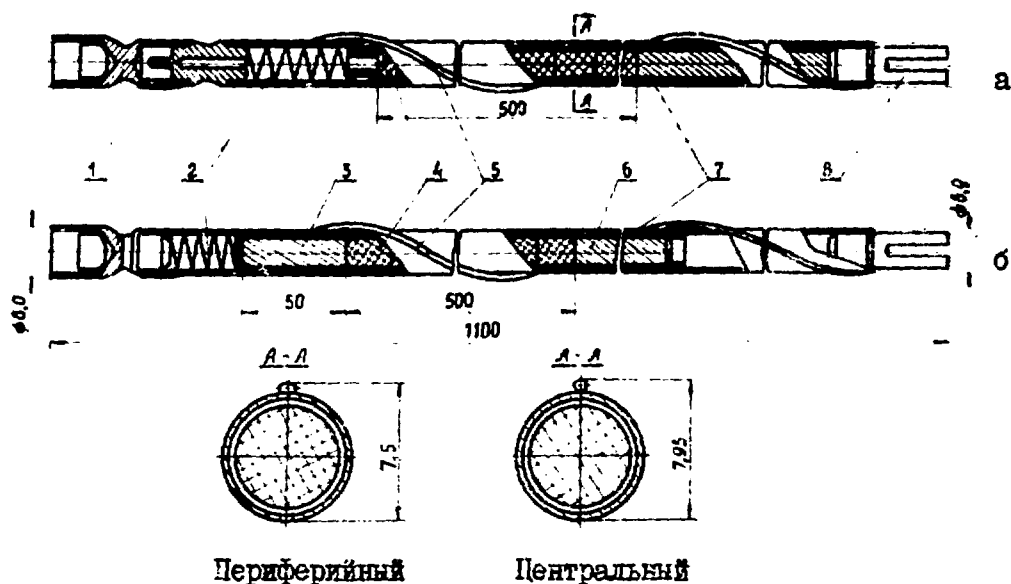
Принципиальная схема опытных твэлов с натрий-калийевой (а) и с галлиевой (б) теплопроводящими прослойками: 1 - верхняя заглушка; 2 - пружина; 3 - верхний отрагатель; 4 - сердечник; 5 - дистанционирующая проволока; 6 - нижний отрагатель; 7 - оболочка; 8 - нижняя заглушка
